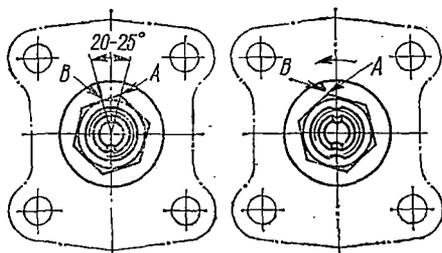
Регулировка осевого зазора в подшипниках ступицы левого переднего колеса
